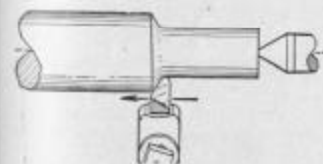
Emplai de l'outil à tourner à coupe de la droite
